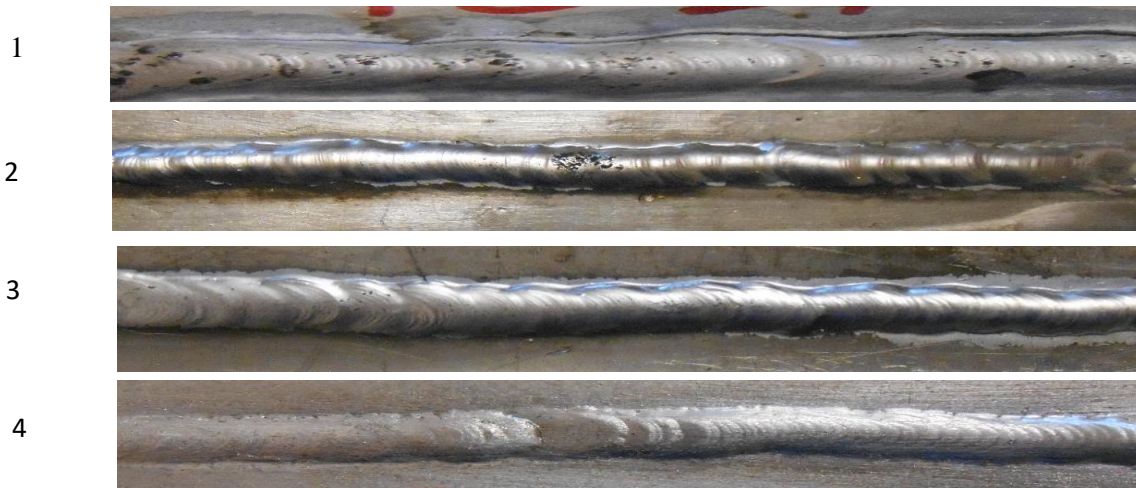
Фрагменты валиков на тонколистовых металлоконструкциях, наплавленных полуавтоматом и автоматом: 1 – валик, полученный при сварке с управляемой импульсной подачей электродной проволоки; 2, 3 (стыковой шов); 4 (автоматический режим) – валики, полученные при дозированной подаче электродной проволоки
